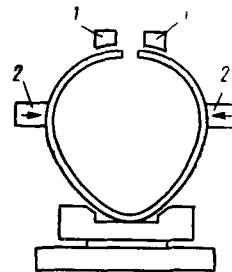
Положение заготовки трубы при контактной сварке оплавлением
